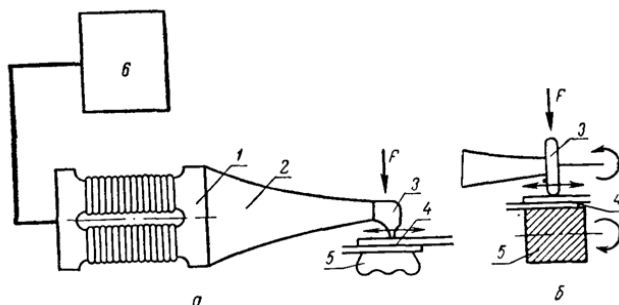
Принципиальная схема ультразвуковой точечной (а) и шовной (б) сварки:
